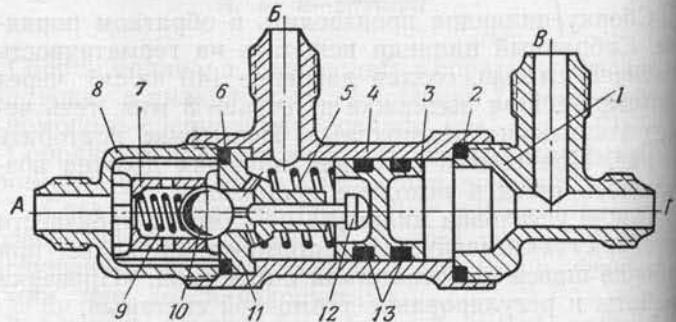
Гидрозамок цилиндра носовой стойки шасси и цилиндра щитков-закрылок.
